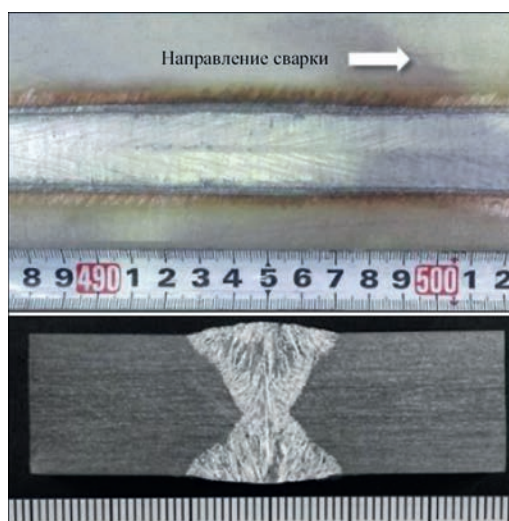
Внешний вид валика сварного шва и макроструктура стыкового соединения US-2209 / PF-S1D (1G)
